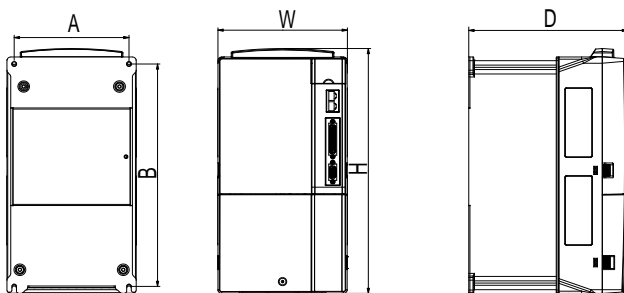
Габаритные размеры приводов типоразмеров F, F2
